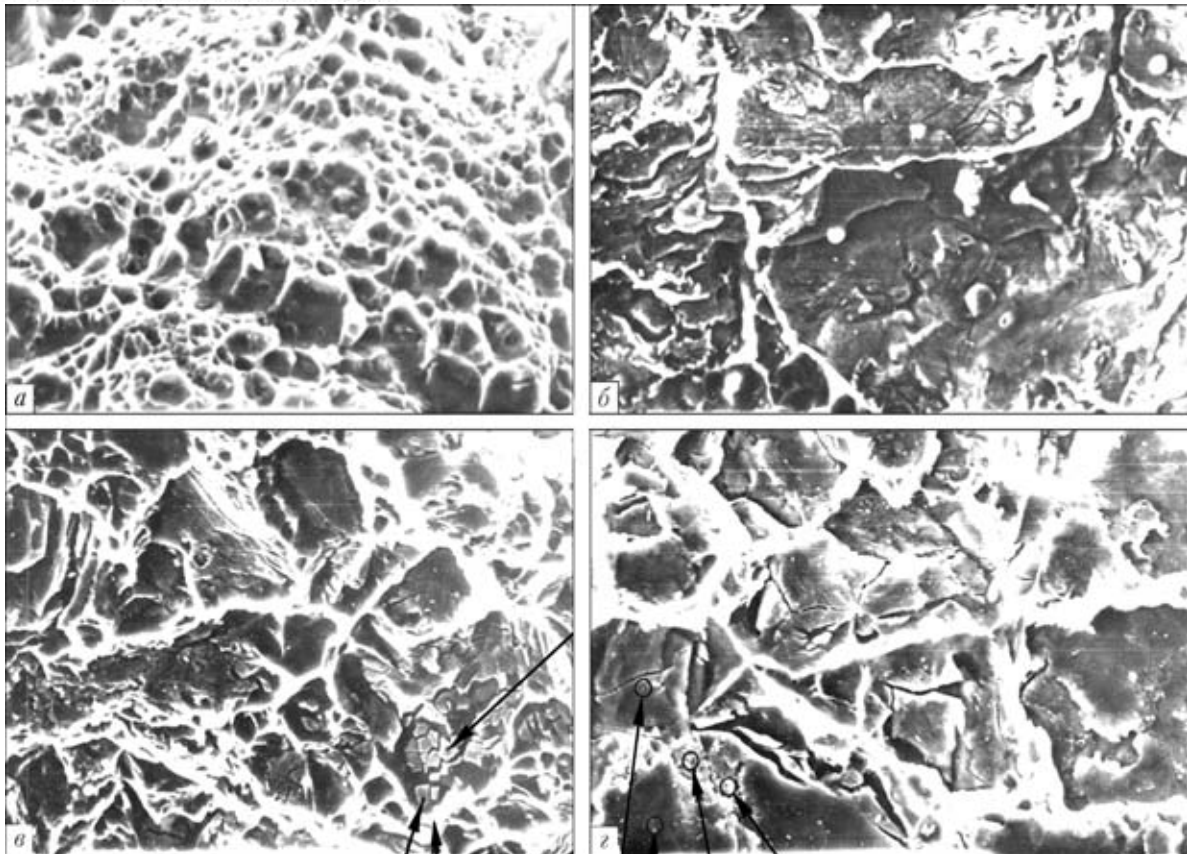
Микроструктура излома сварного соединения Ст3+АК4 со стороны алюминия, полученного КСС непрерывным оплавлением на I (а, в, X680) и II режимах (б, X300; г, X680)
